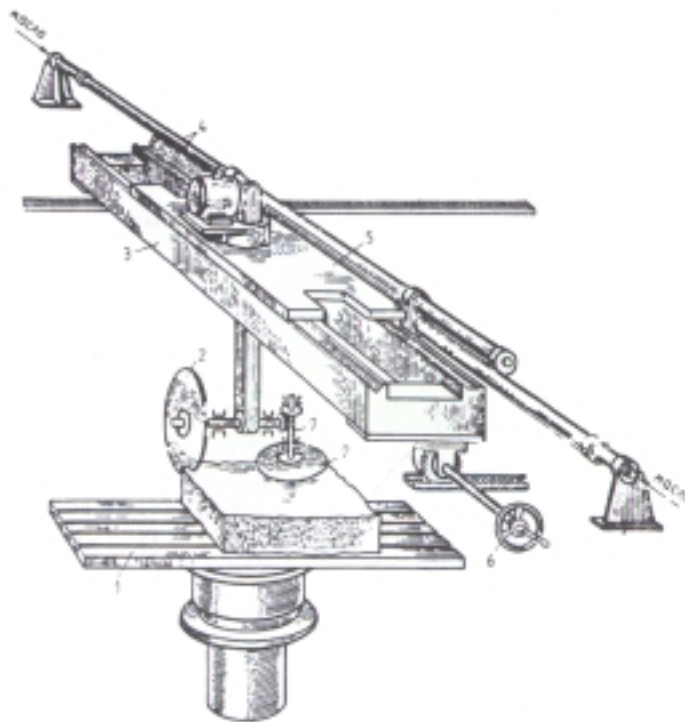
Общ вид на фрезерно-обрязваща машина “СМР – 015” (Русия)
